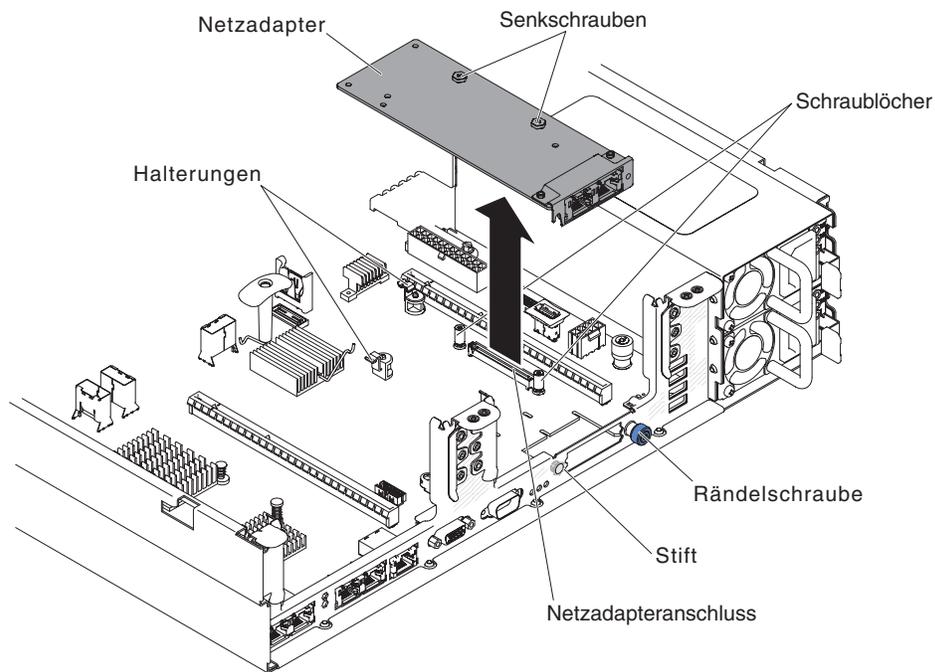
Netzadapter mit zwei Anschlüssen entfernen
